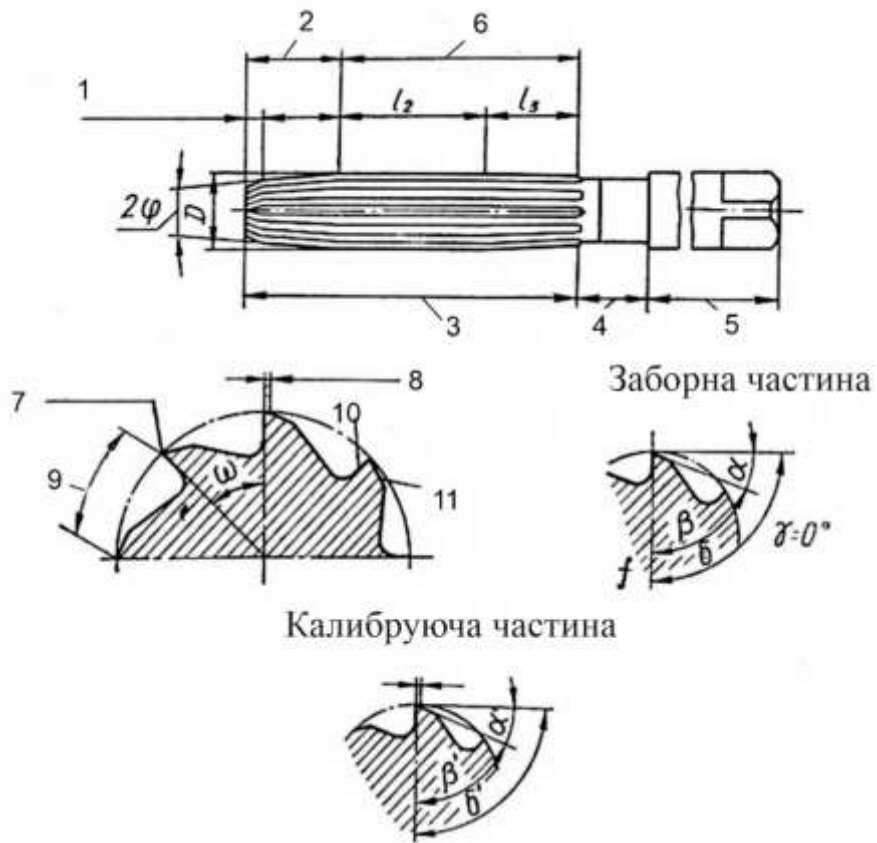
Конструкція ручної цільної розгортки: 1 – напрямний конус; 2 – ріжуча частина; 3 – робоча частина; 4 – шийка; 5 – хвостовик; 6 - калібруюча частина; 7 - головна ріжуча кромка; 8 – стрічка; 9 – крок зубів; 10 – передня поверхня; 11 – задня поверхня.
